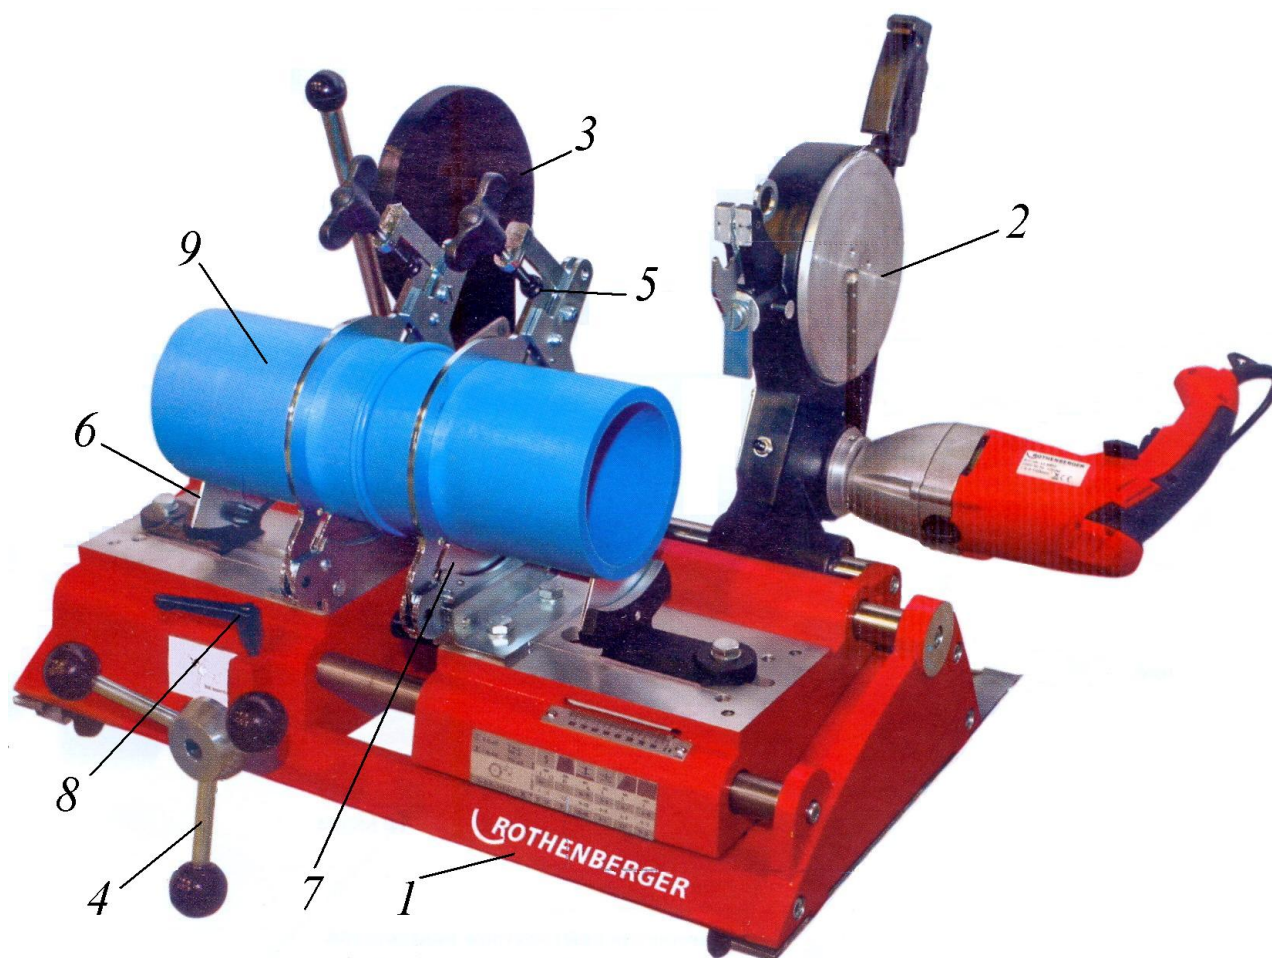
Машина для сварки пластмассовых труб ROWELD P 160 SANI-LINE: 4 – рукоятка привода сжатия; 8 – фиксатор усилия; 9 - свариваемая труба (остальные обозначения в тексте)
